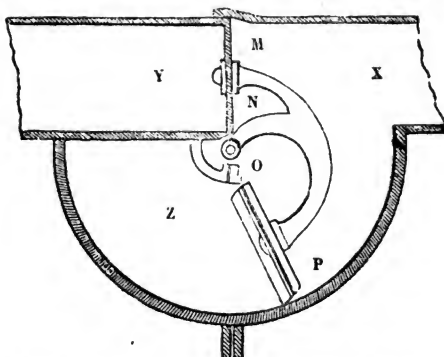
Vue (d'en haut) de la soupape d'entrée, fermée par son couvercle.
